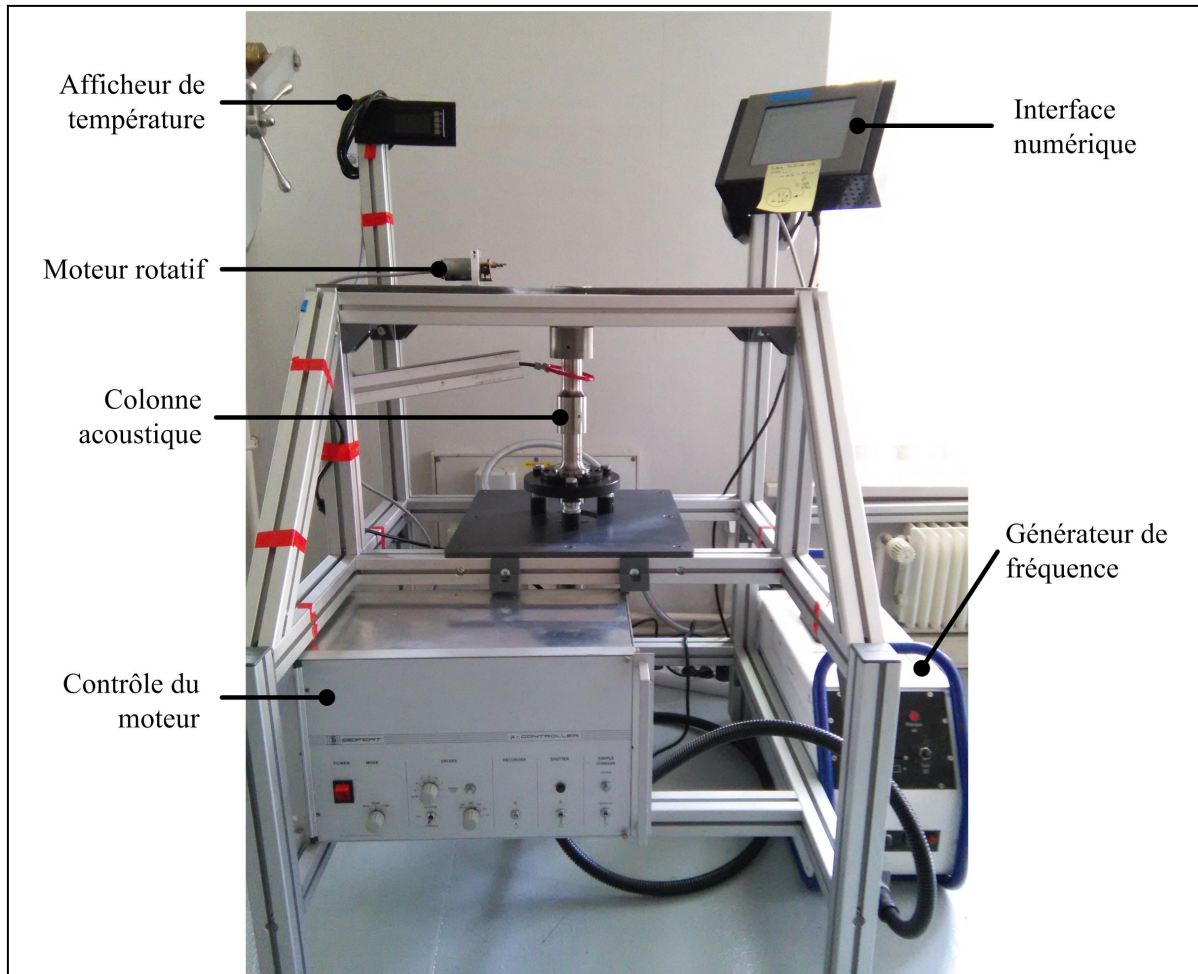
Photographie d'une vue d'ensemble du dispositif de grenaillage ultrasonique
